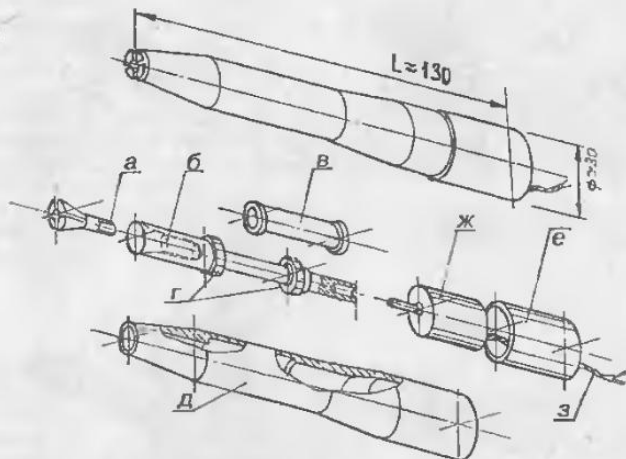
Конструкция бормашины: а - цанга; б - вал; в - распорная втулка; г - шарикоподшипники; д - корпус; е - крышка; ж - электродвигатель; з - электрошнур
